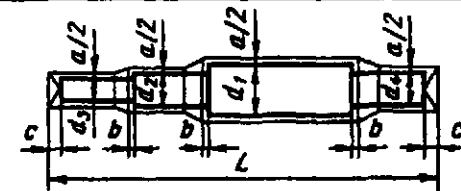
Схема штамповки радиальным обжатием; с – подача заготовки
